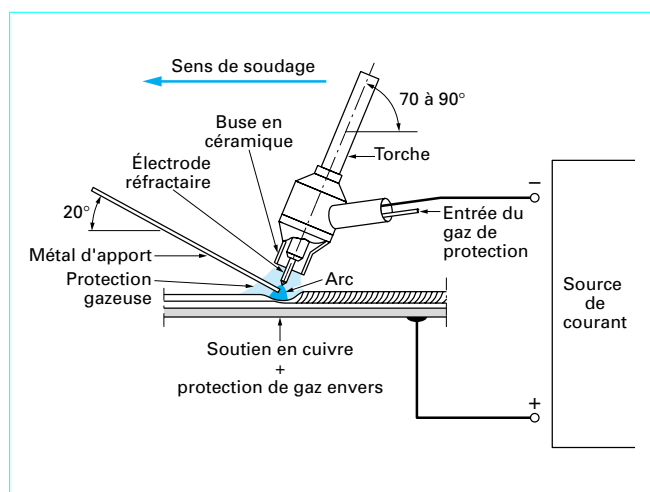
Principe du soudage (manuel) à l'arc électrique avec électrode réfractaire (GTAW ou TIG), d'après [17]
